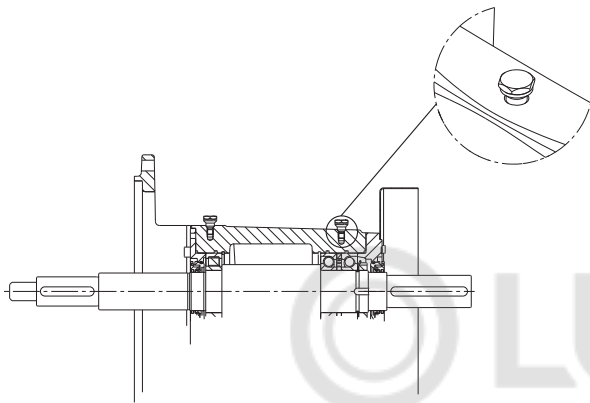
Корпус подшипника с местами для установки датчиков SPM
